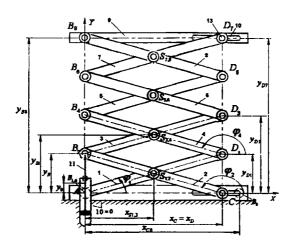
Кинематическая схема рычажного механизма ножничного подъемника
